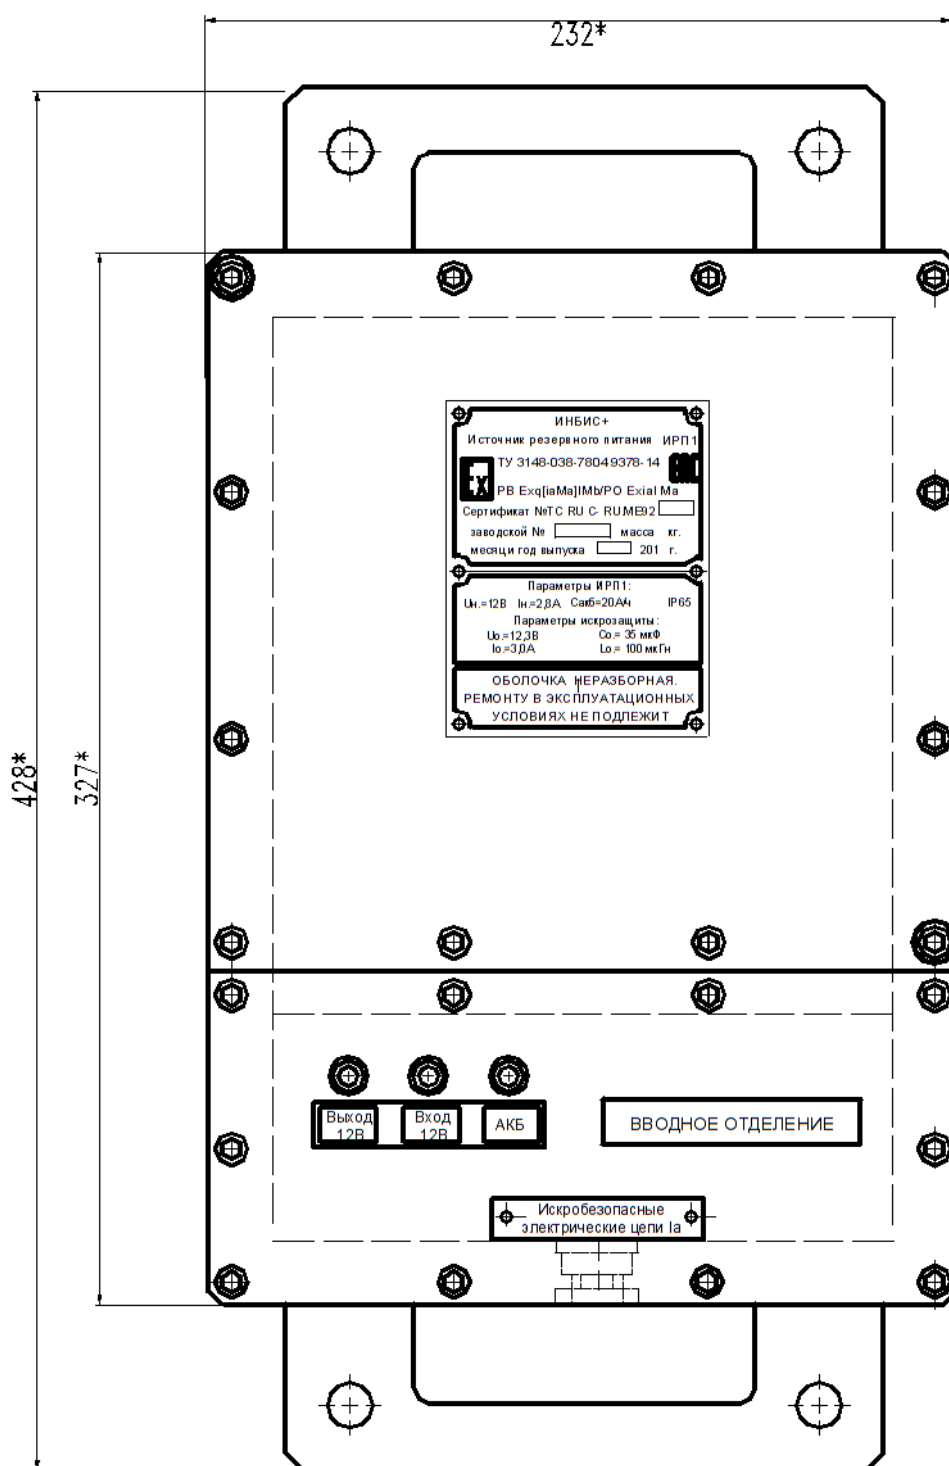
Общий вид и габаритные размеры источника резервного питания ИРП1
